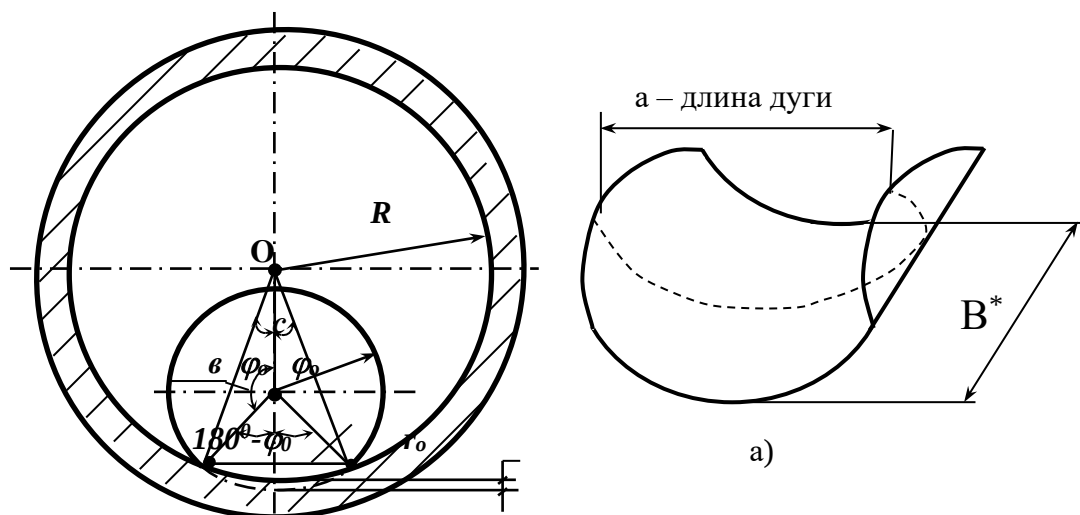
Схема контакту внутрішньої циліндричної поверхні з ЕПАІ.
